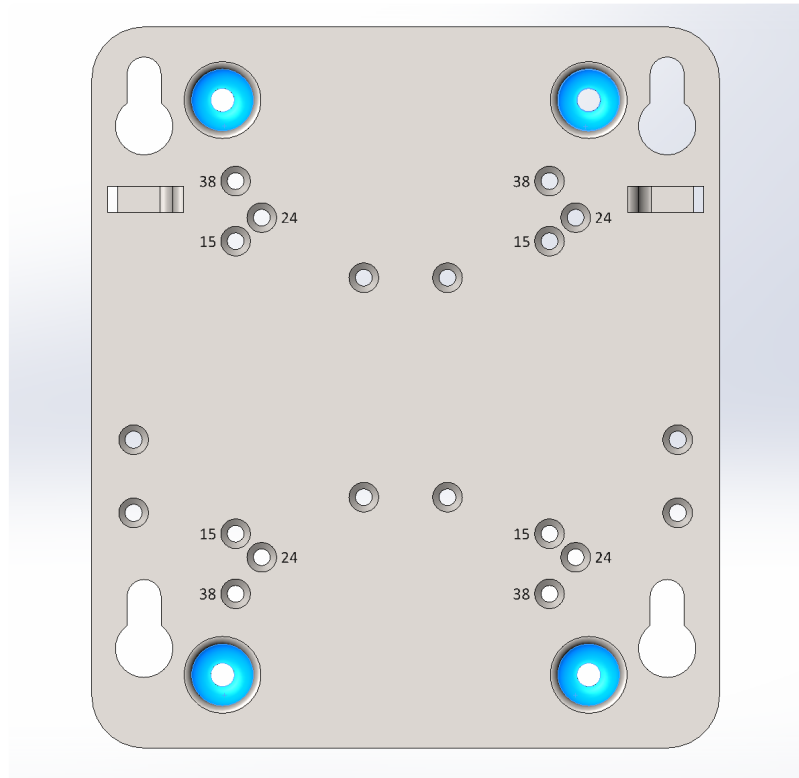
Отверстия для крепления монтажной пластины к стене/потолку
